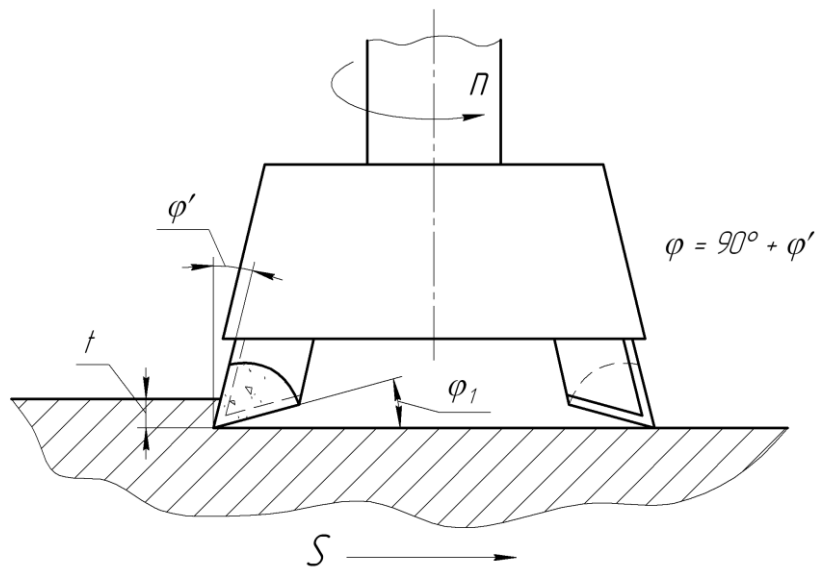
Схема видалення припуску з урівноваженням складової сили різання P_Y при торцевому фрезеруванні
